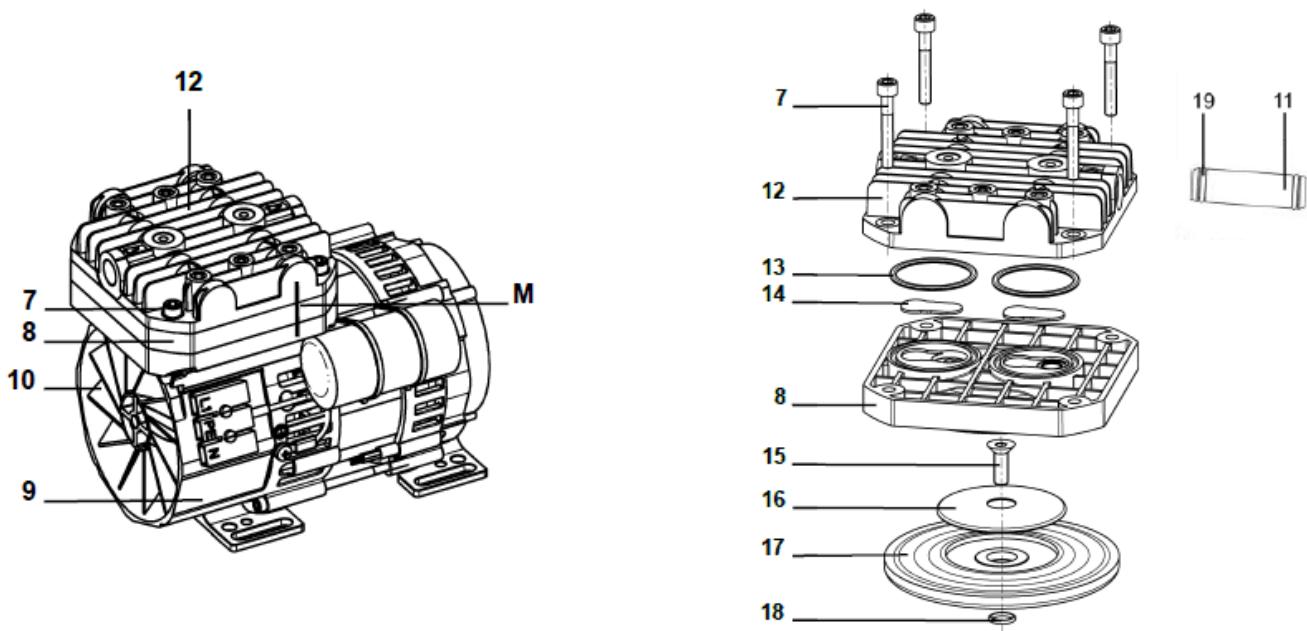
(а) Внешний вид и детализировка головки вакуумного насоса DV
